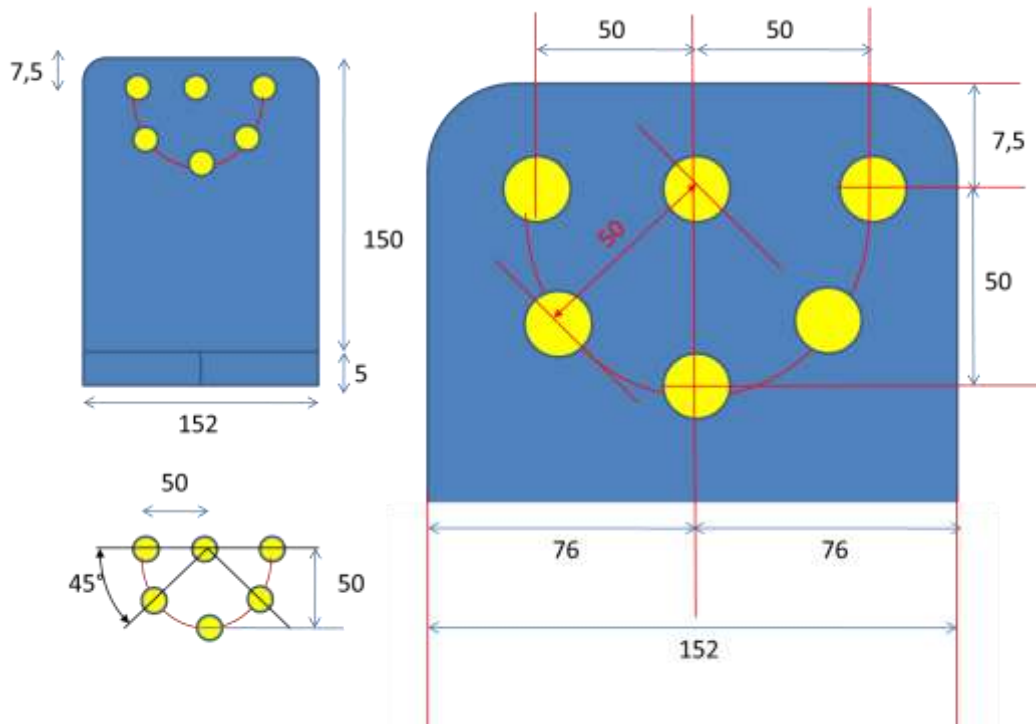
Pormenor da furação do suporte do dispositivo.
